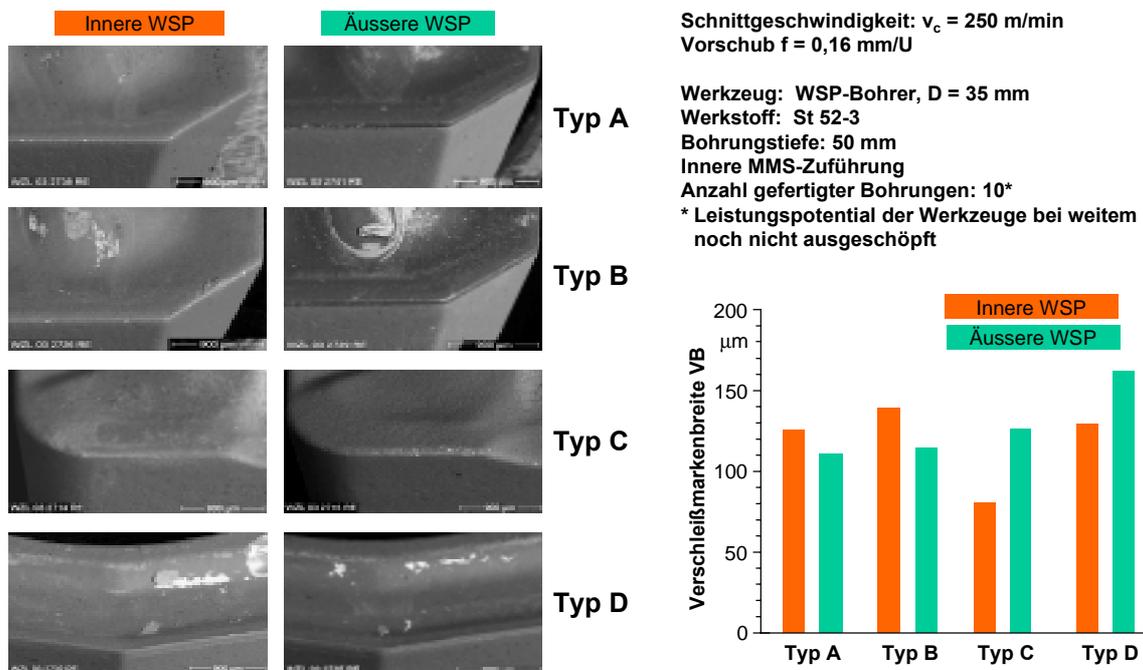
Ausführungsvarianten der beim Trockenbohren mit MMS eingesetzten mit Wendeschneidplatten bestückten Bohrwerkzeuge
